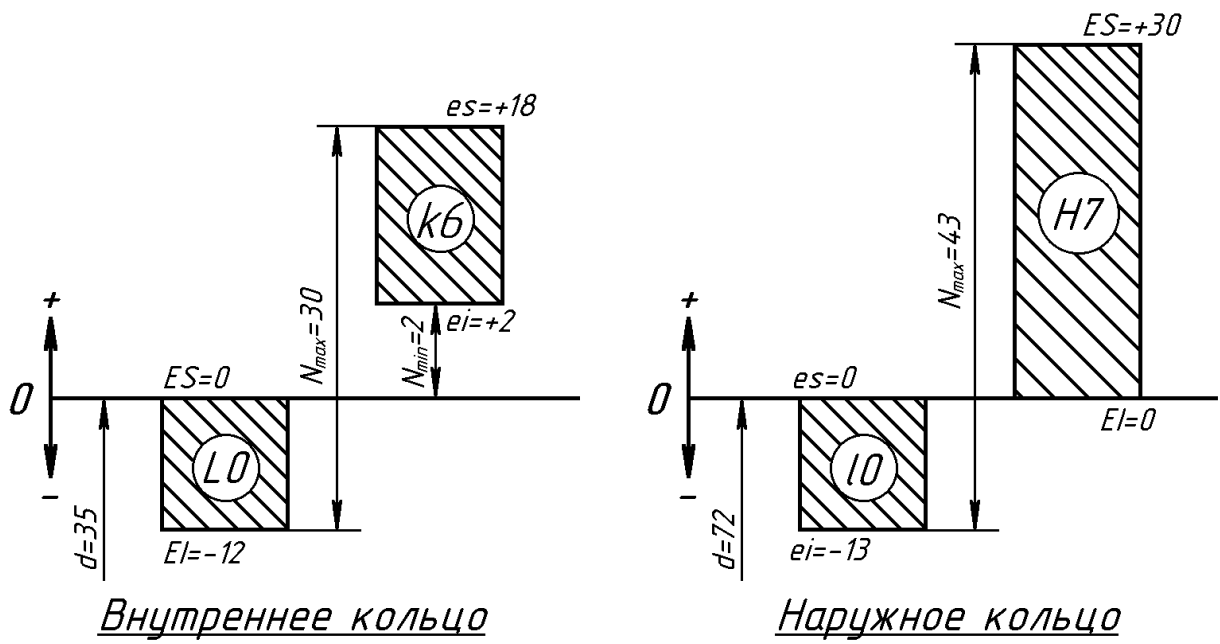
Схемы расположения полей допусков колец подшипников качения
